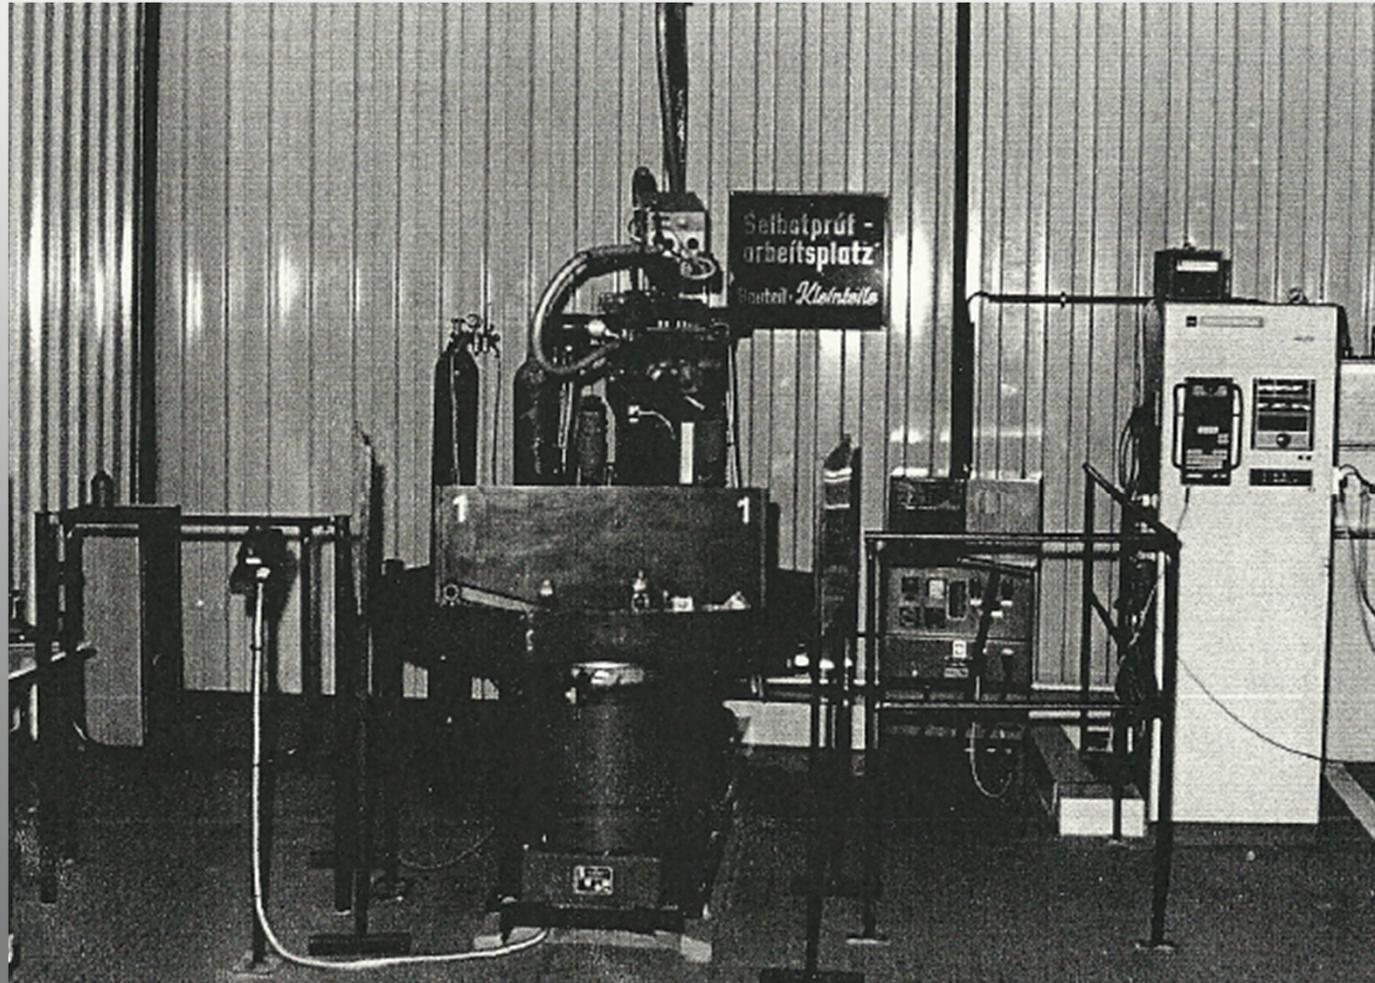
Roboterschweißplatz für Kleinteile
